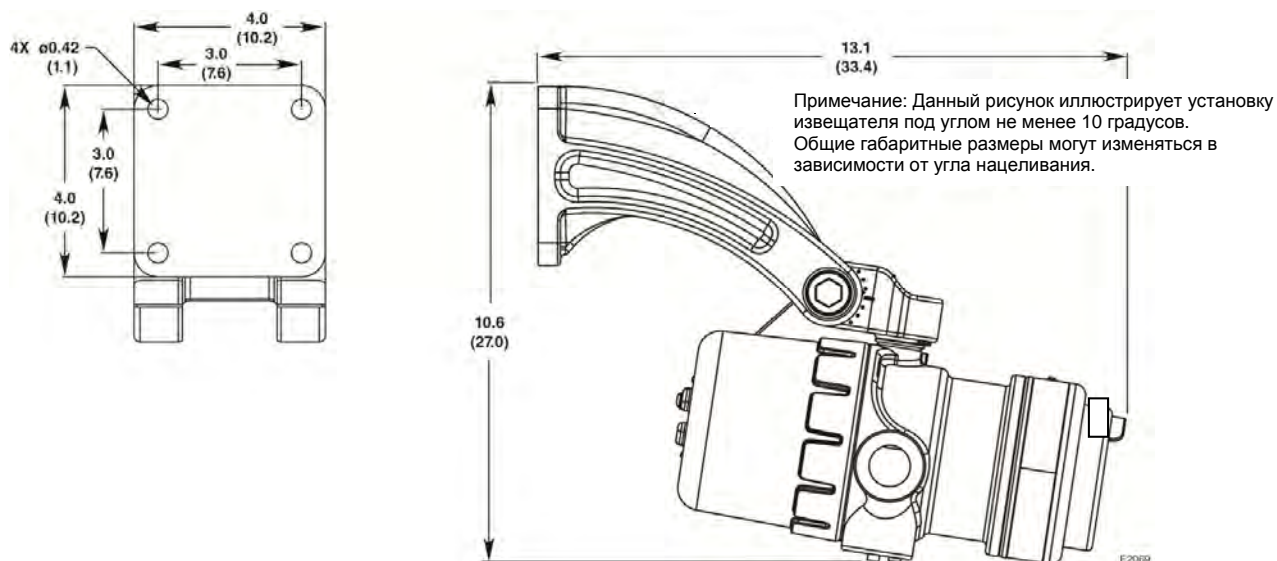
Габаритные размеры извещателя с монтажным кронштейном Q9033 в дюймах (см).
